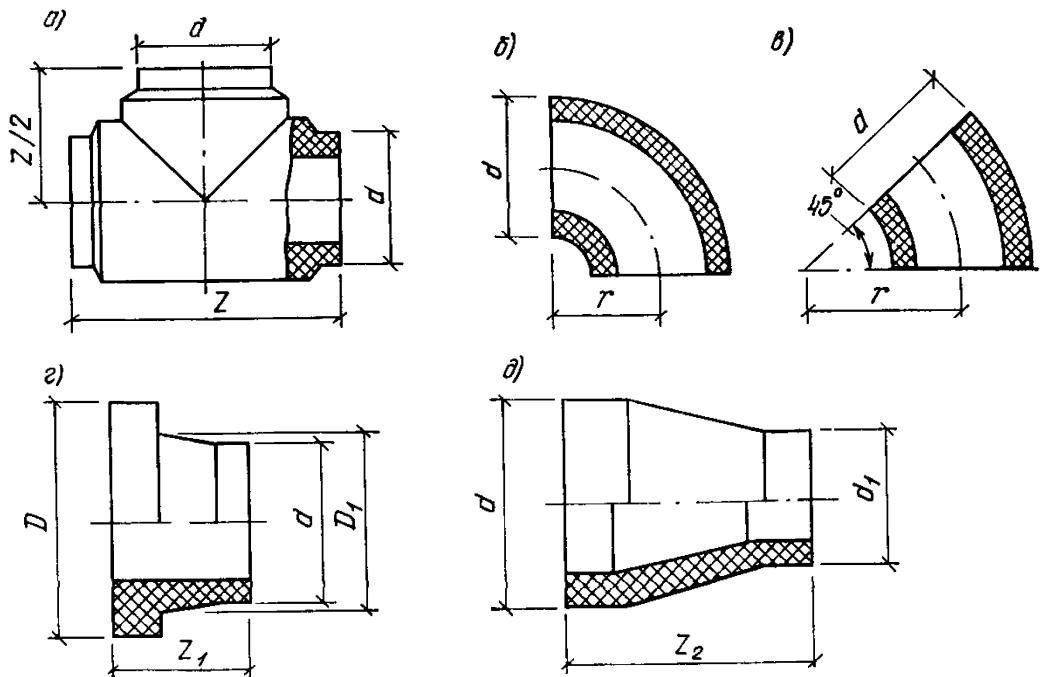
Соединительные детали из ПНД, изготовленные методами литья под давлением, прессованием и намоткой:
